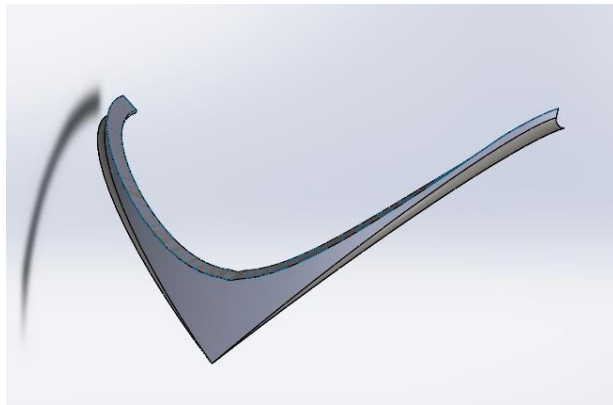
Mitad del volumen de soldadura del injerto (Fuente: Propia)
